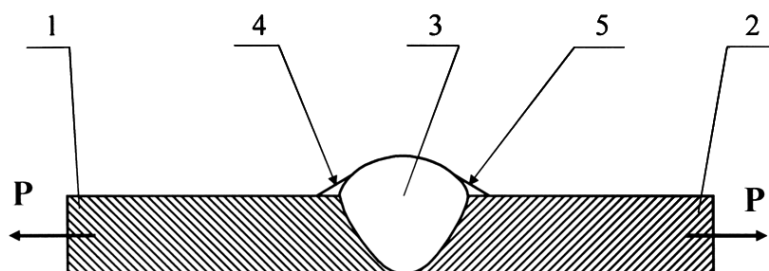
Схема гибридного паяно-сварного соединения, обеспечивающего снижение концентрации напряжений: 1 и 2 – соединяемые заготовки, 3 – стыковой сварной шов, 4, 5 – напайки из материала с более низким модулем упругости, чем у основного материала, P – приложенное усилие
